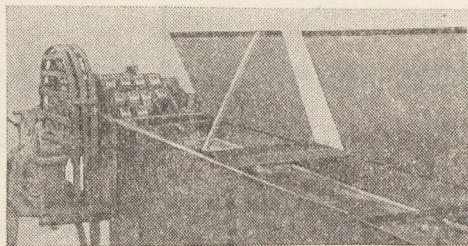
Общий вид машины для покрытия банок с консервами вазелином
